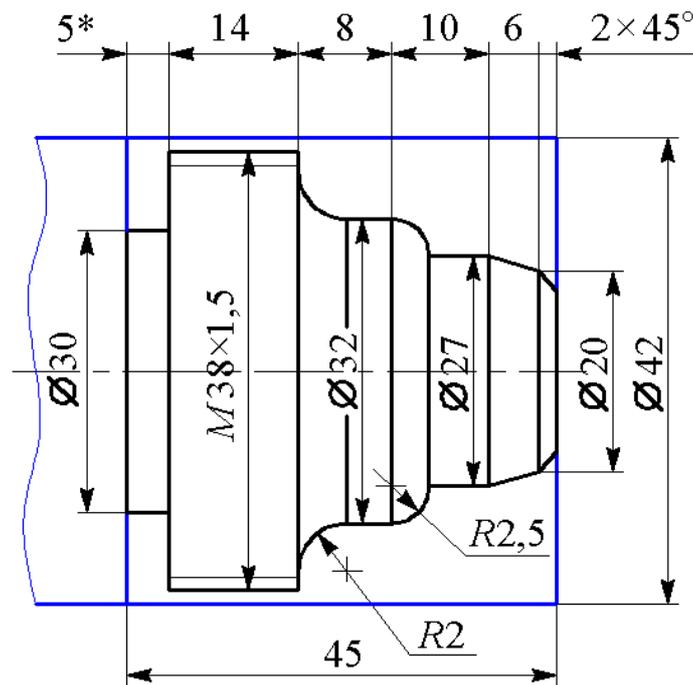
Эскиз обрабатываемой детали для подгруппы 2
